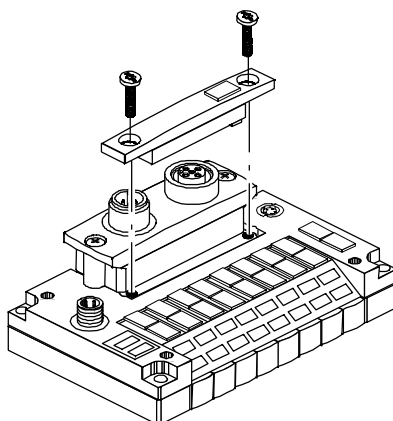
/2: Smontaggio e montaggio del modulo interruttori
